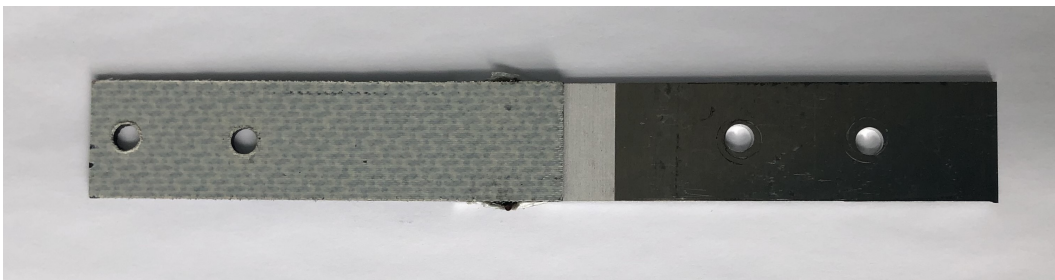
Herstellung eines TP FMHs mittels Single-Spot-Schweißen
